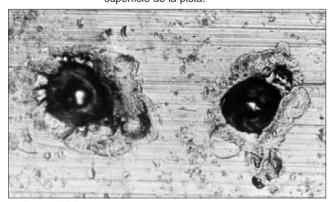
Componente: Anillo interno de rodamiento rígido de una hilera
